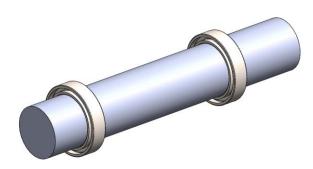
Diseño en solid works. Rodamientos 6203 instalados en una flecha
